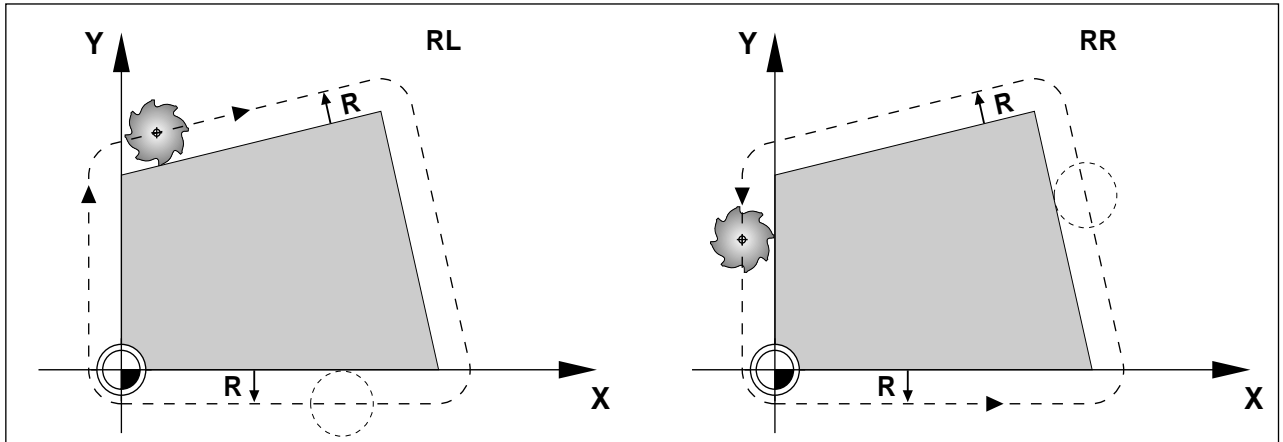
Das Werkzeug verfährt zum Fräsen links (RL) oder rechts (RR) von der Kontur
